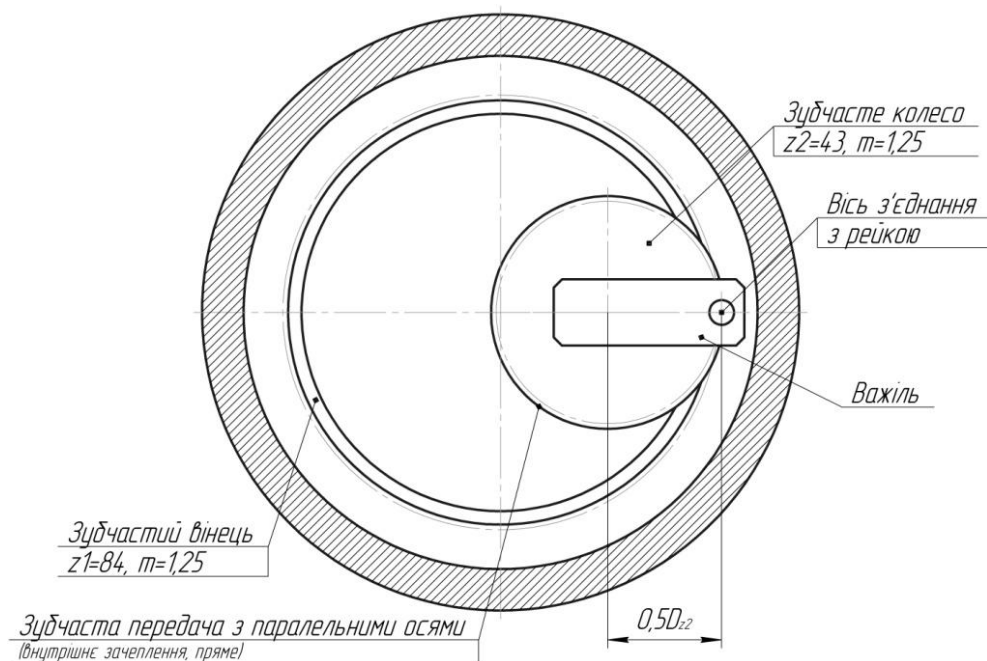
Механізм передачі руху від зубчастого колеса до зубчастої рейки
